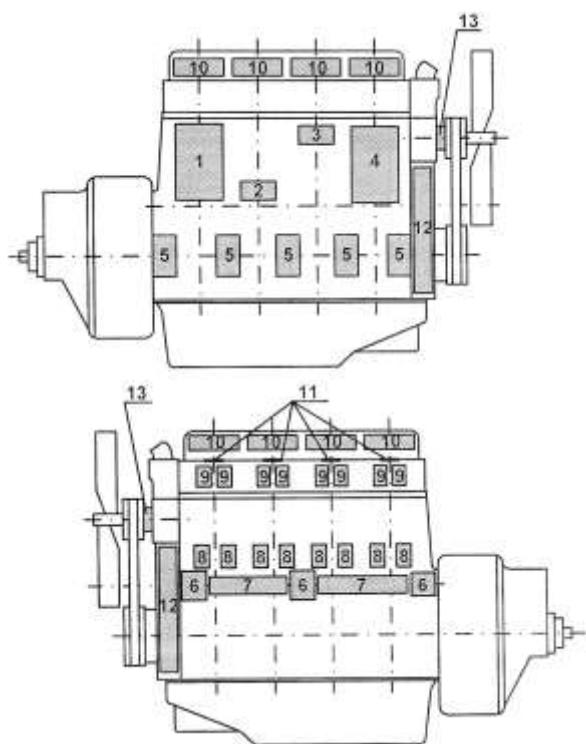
Схема прослуховування двигуна: 1 – поршень – циліндр; 2 – поршневе кільце – канавки на поршні; 3 – поршневий палець – втулки шатуна; 4 – колінчастий вал – шатунний підшипник; 5 – колінчастий вал – корінний підшипник; 6 – розподільний вал – підшипник; 7 – кулачок розподільного валу; 8 – штовхач – втулка штовхача; 9 – стрижень клапана – направляюча втулка; 10 – бойок коромисла – стрижень клапана; 11 – клапан – дно поршня; 12 – розподільні шестерні; 13 – водяний насос.
